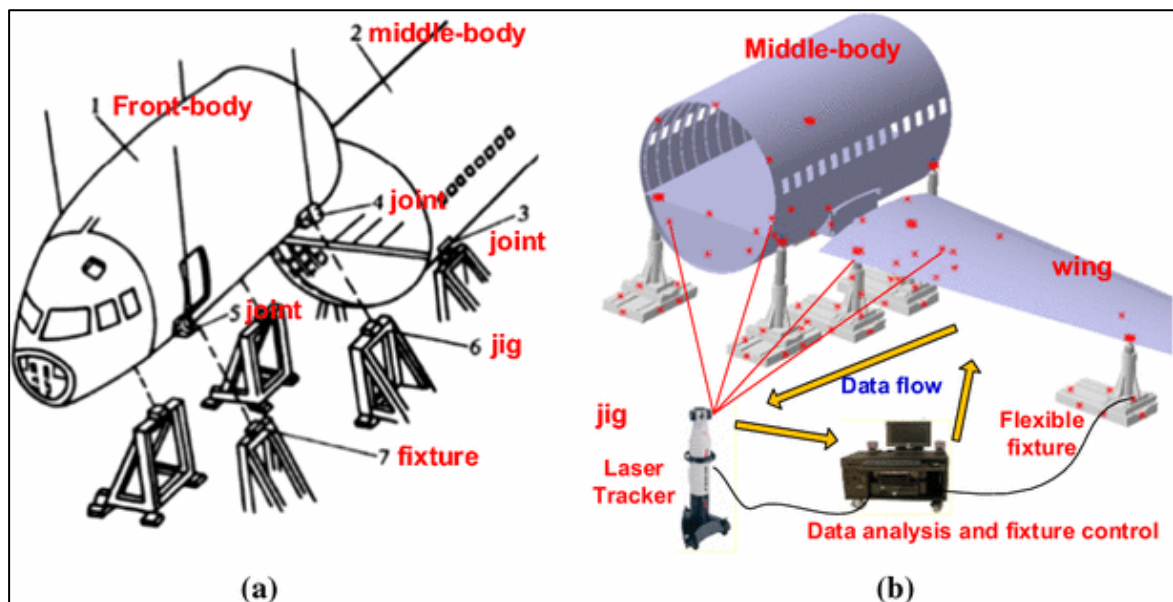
L'approche traditionnelle (a) et la technologie d'assemblage assistée par la mesure (b) pour l'assemblage à grande échelle
